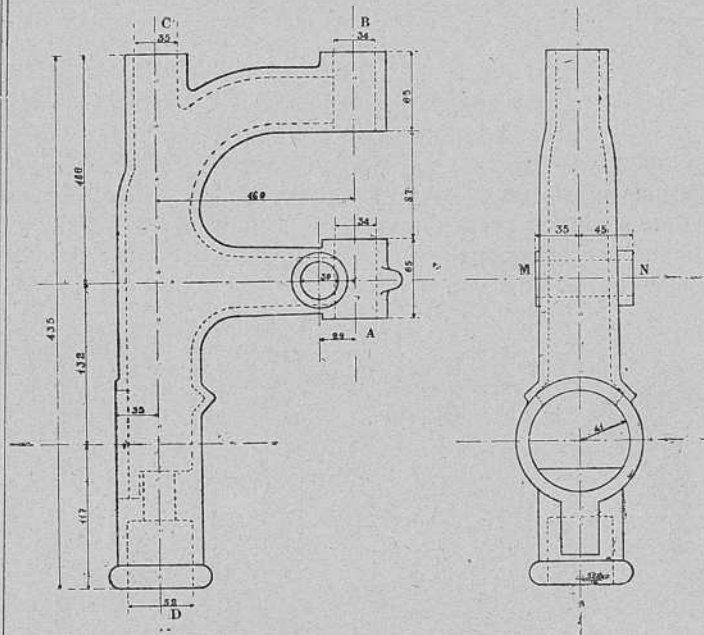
Croquis acotado de una pieza que se ha de trazar.
